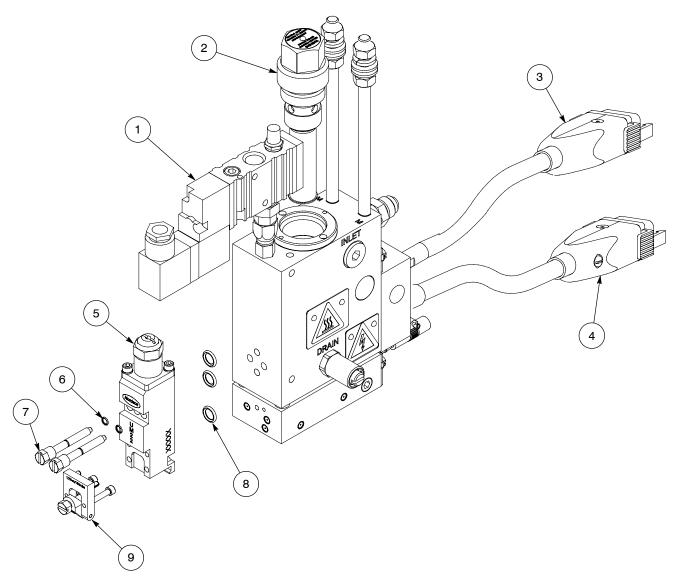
Pièces de rechange du pistolet (la figure représente un module UM22 standard réglable)
